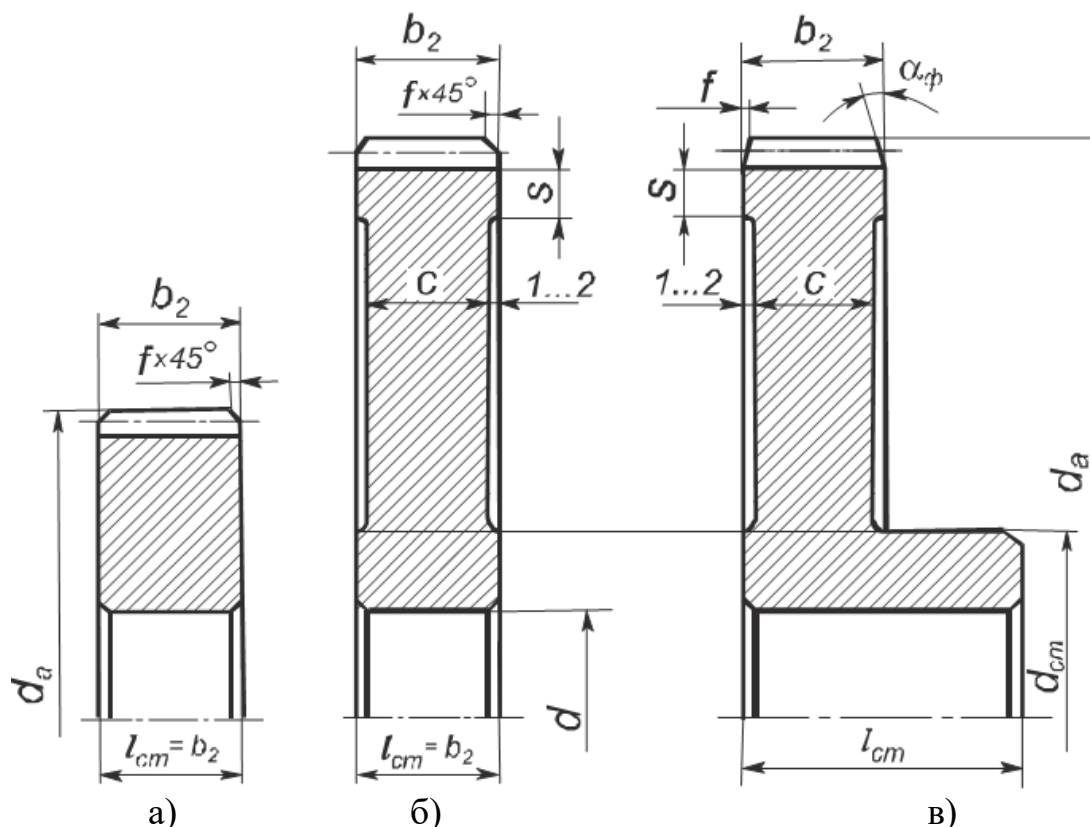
Размеры кованных или штампованных цилиндрических зубчатых колес
